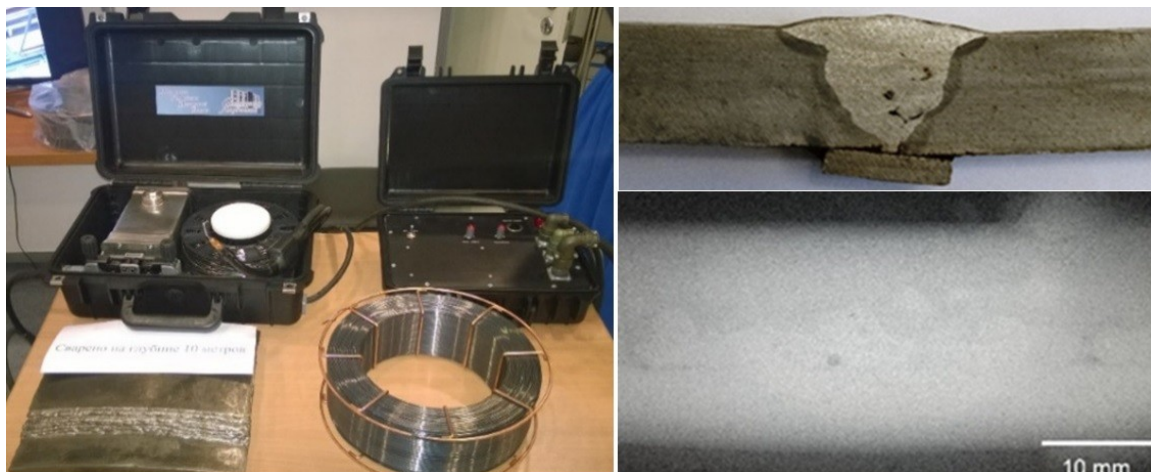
Портативный сварочный комплекс, порошковые проволоки, опытное сварное соединение, макроструктура и рентгеновский контроль шва толщиной 21,3 мм из бейнитной стали API X70.
